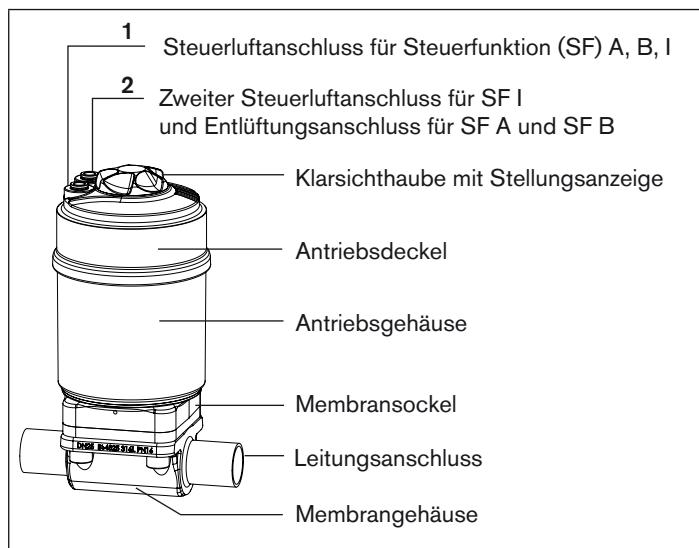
Kolbengesteuertes Membranventil, Aufbau und Beschreibung
